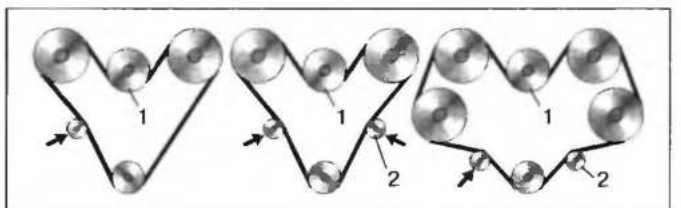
Основные схемы ременного привода распределительного механизма V-образных двигателей: 1 — шкив привода вспомогательных агрегатов; 2 — паразитный ролик
